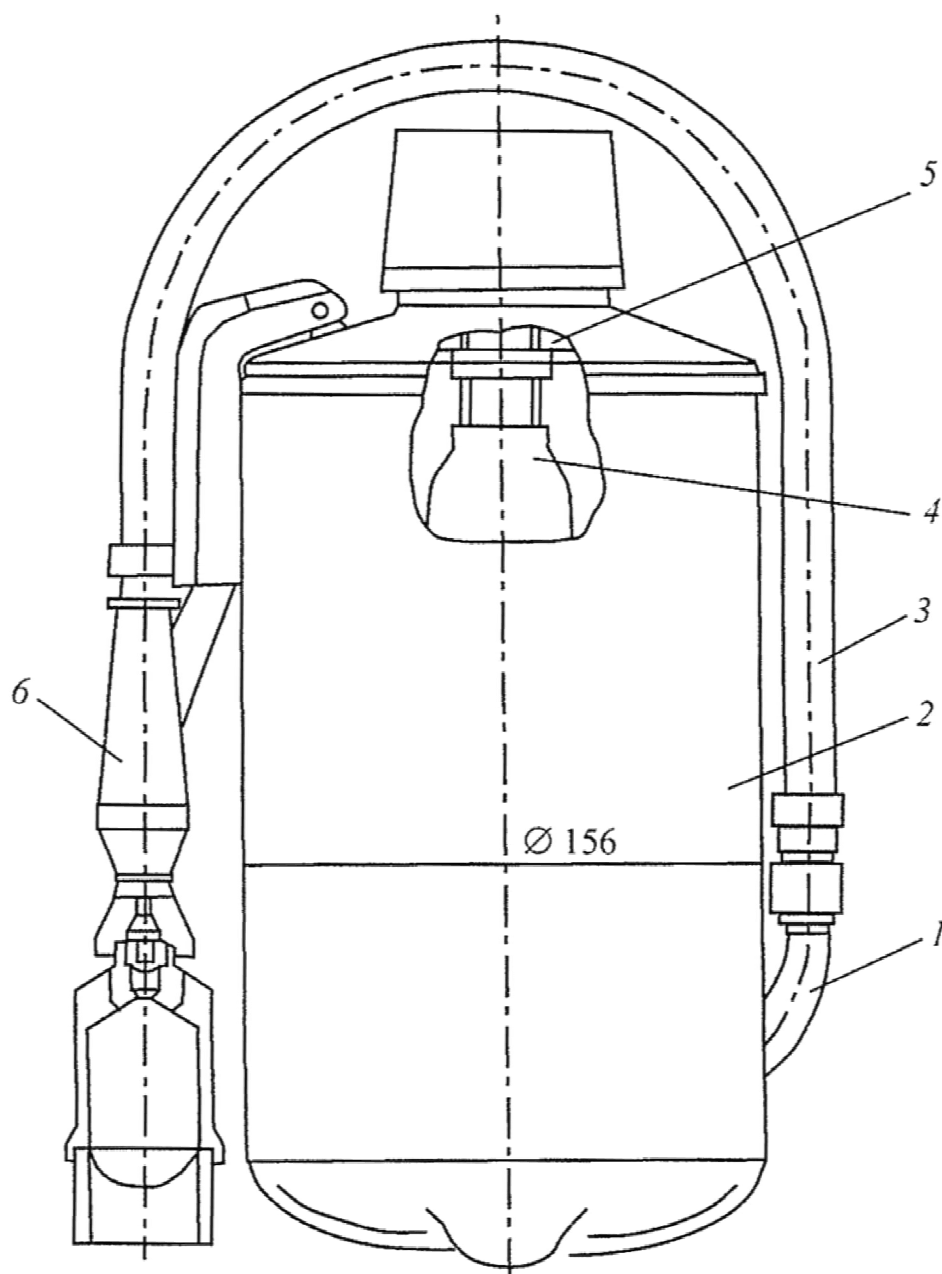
Огнетушитель воздушно-пенный ручной ОВП-5: 1 — трубка сифонная; 2 — корпус; 3 — рукав; 4 — баллон для рабочего газа; 5 — крышка; 6 — насадка
